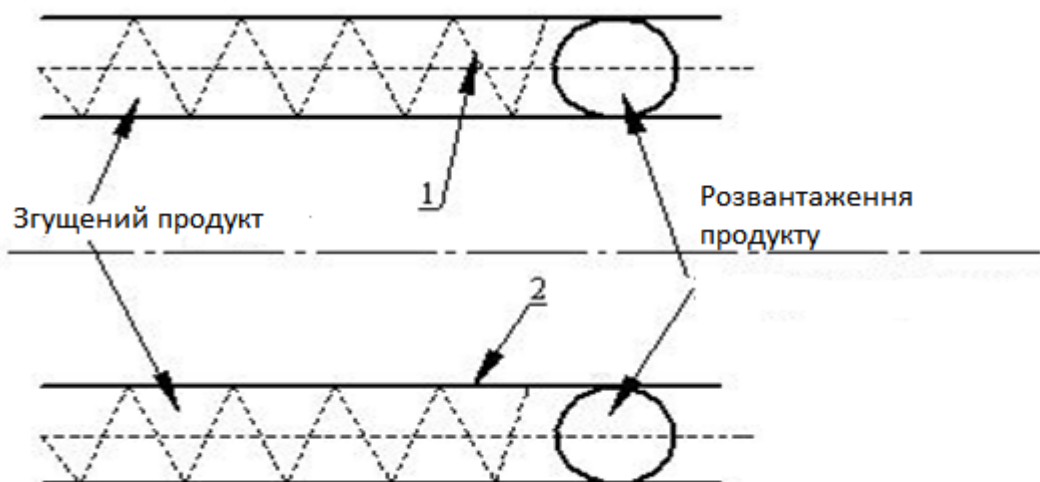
Схема розташування розвантажувального органу базової конструкції: 1 – Шнек; 2 – Корпус шнека; 3 – Вихідний патрубок.
